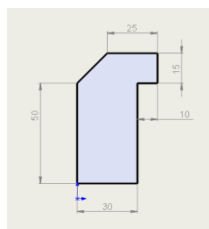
Чертеж для изготовления рулей модели лодки
